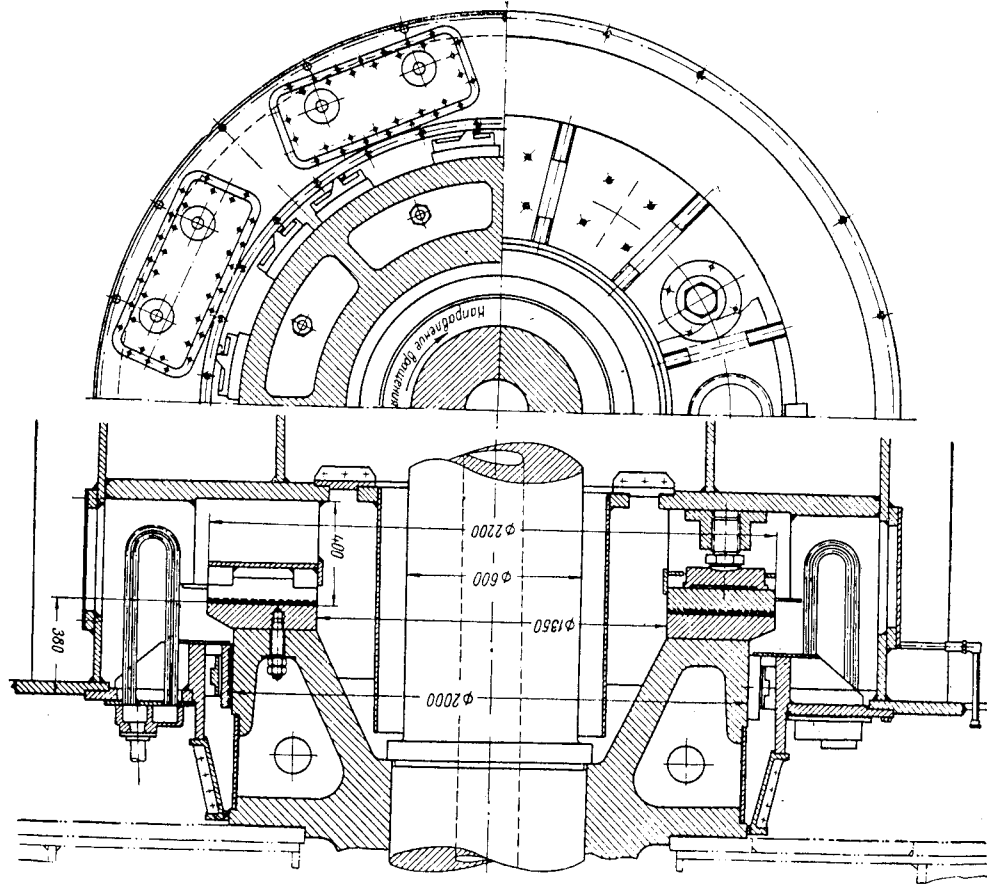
Комбинированный подпятник и направляющий подшипник гидрогенератора
